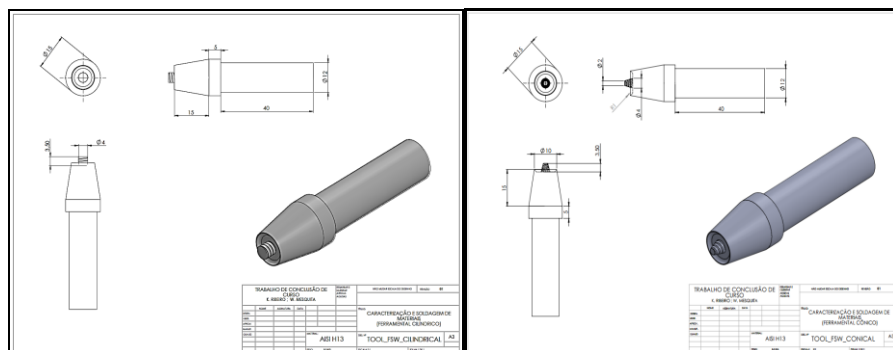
Desenho do ferramental com ponta cilíndrica (à esquerda) e cônica (à direita) fabricado em AISI H13
